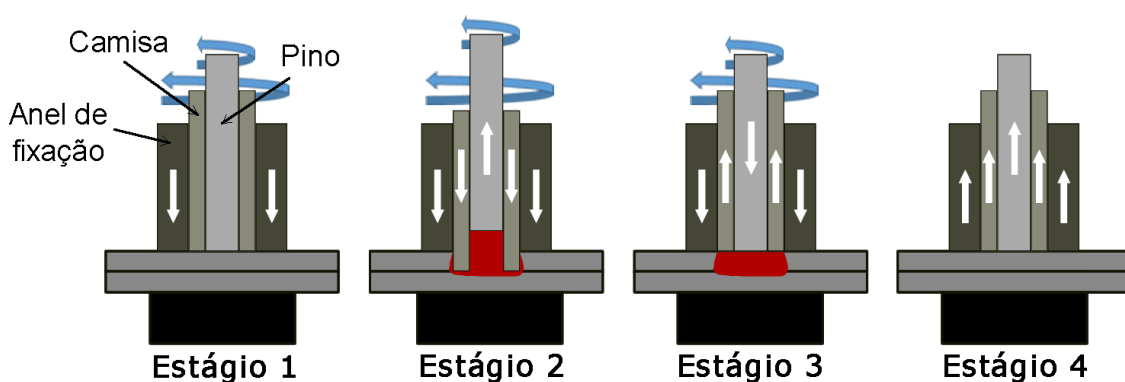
Desenho esquemático indicando as etapas do processo FSpW [2].
